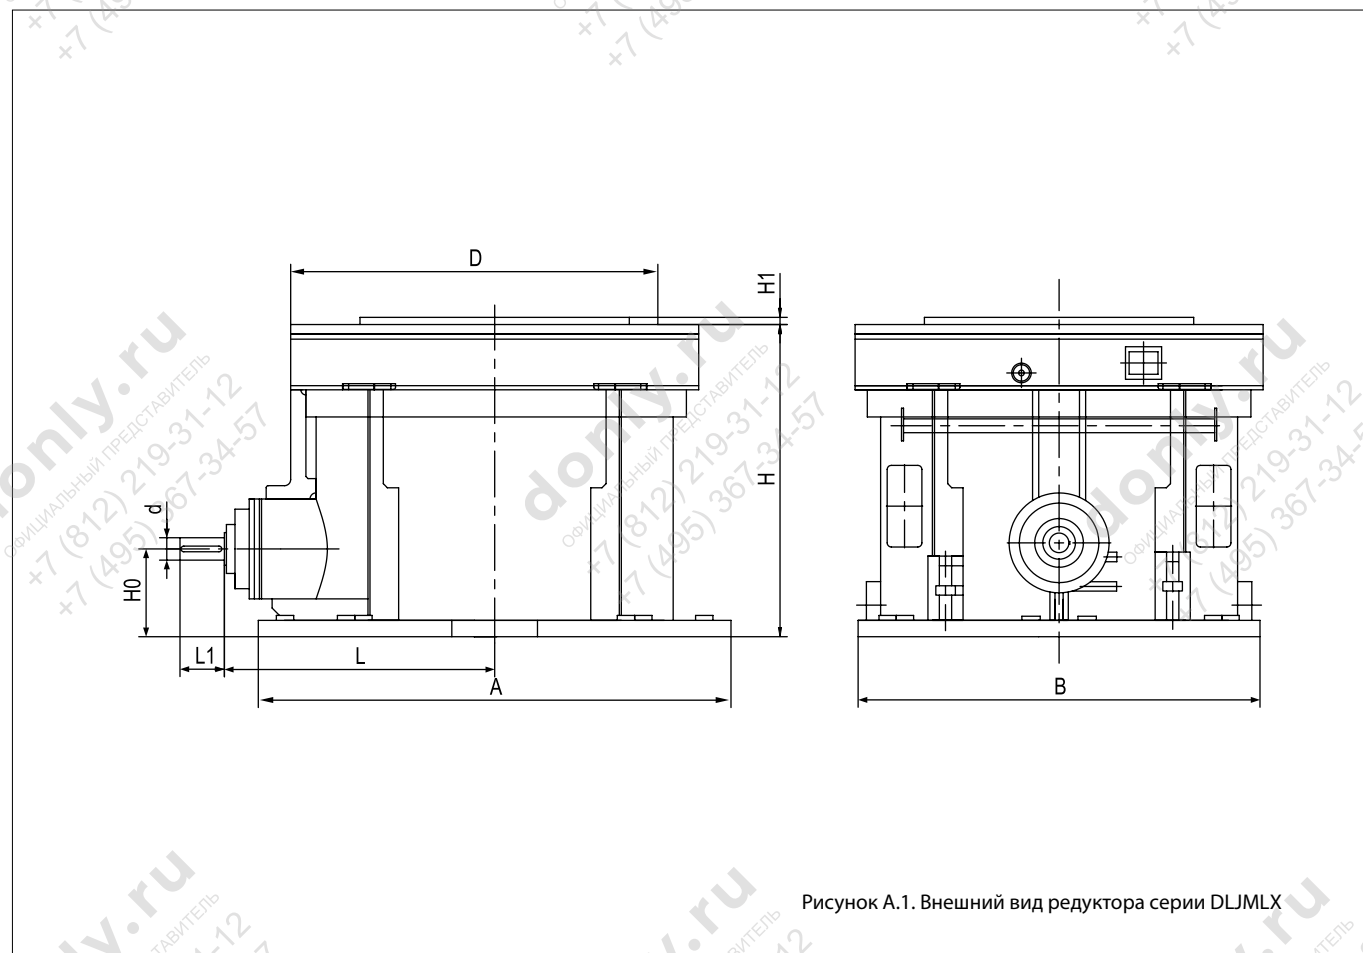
Внешний вид редуктора серии DLJMLX
